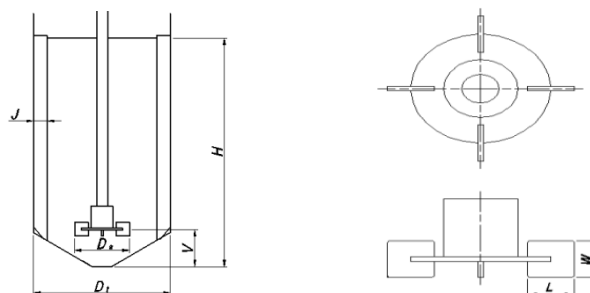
Diseño del reactor de Metóxido: dimensiones.
